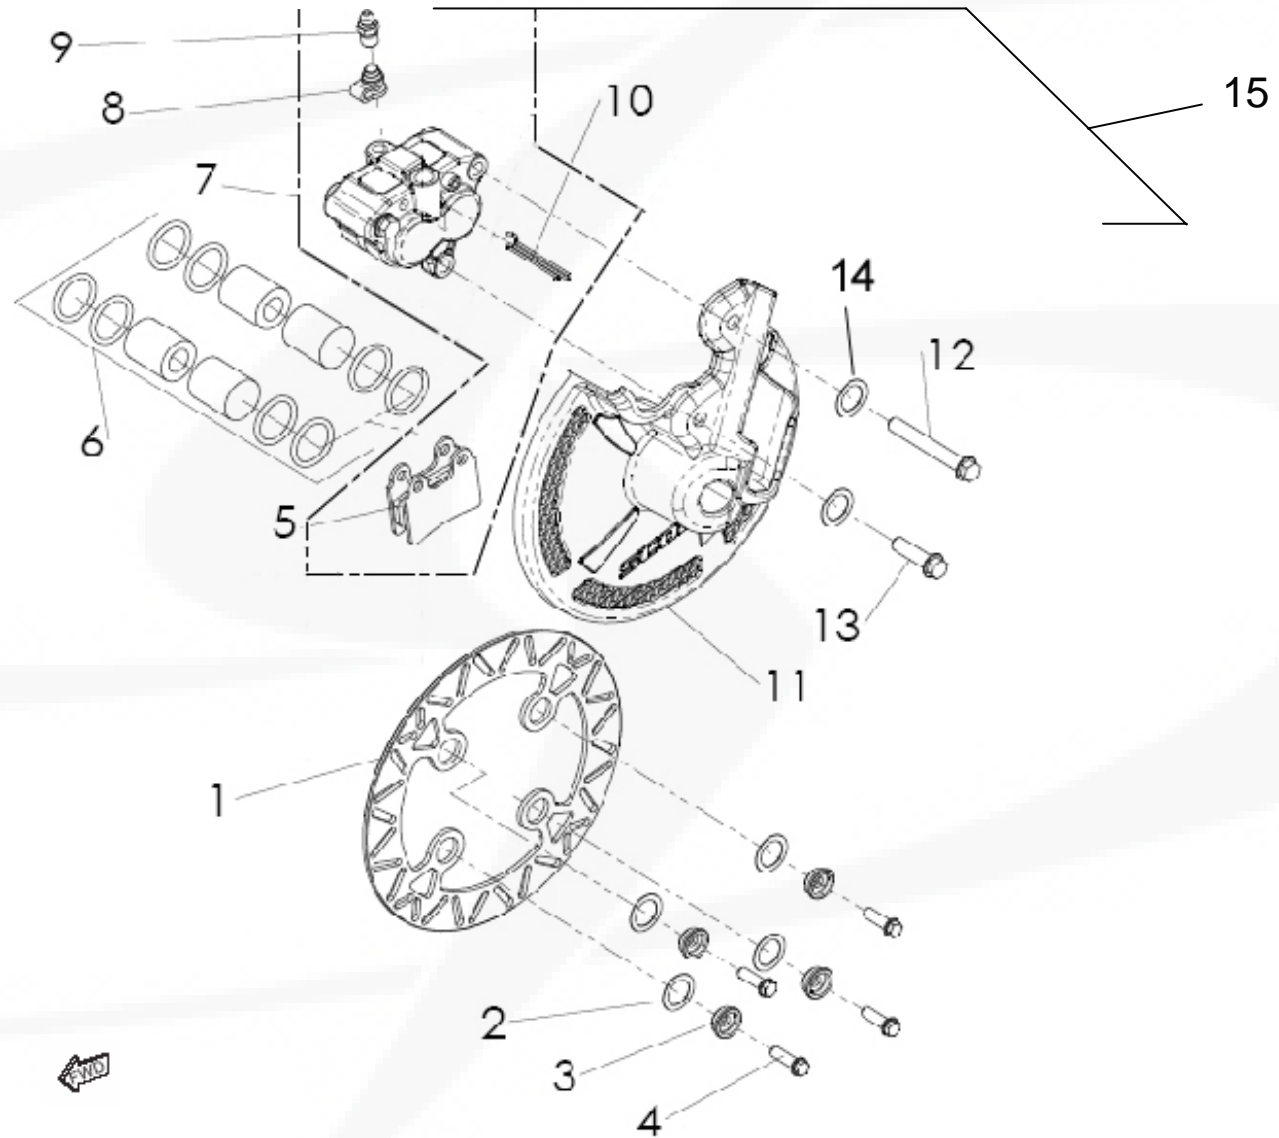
FREIN AVANT / FRONT BRAKE / FRENO DELANTERO
